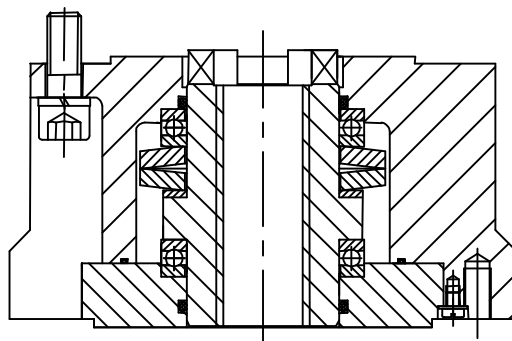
中速缓冲推力盘 Fig. 3 Medium speed buffering thrust attachment
